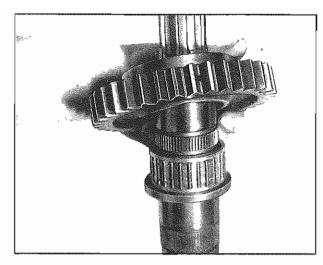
Ingranaggio della 1a marcia 1st gear
